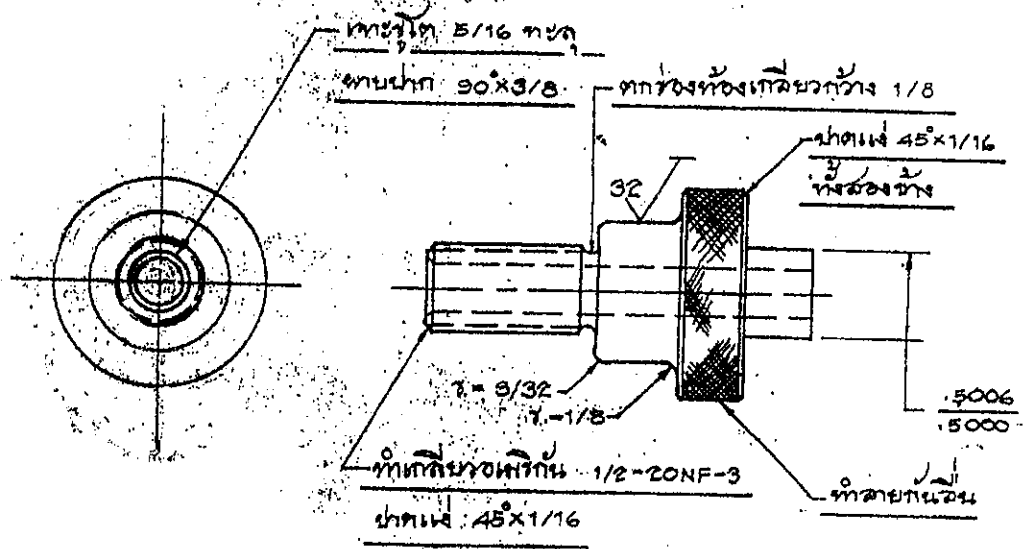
การให้ DIMENSION จาก DATUM
